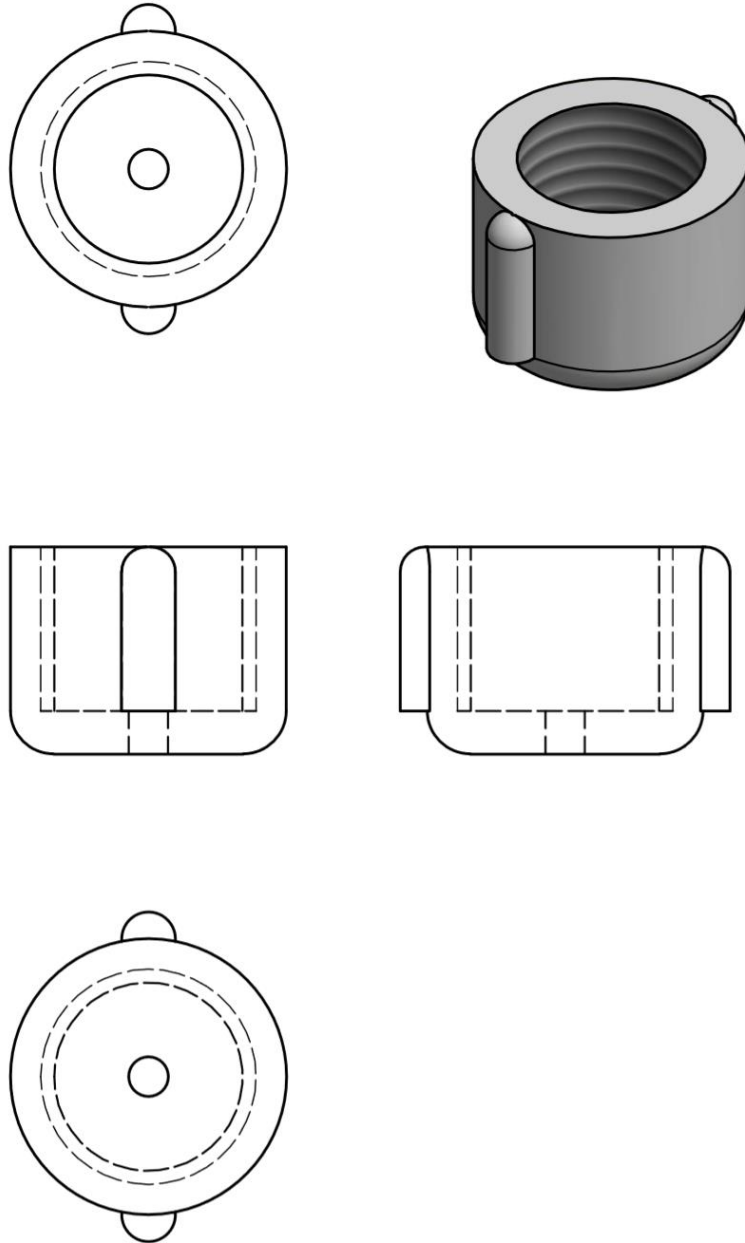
Pieza acople macho, estándar (no se indican dimensiones)
